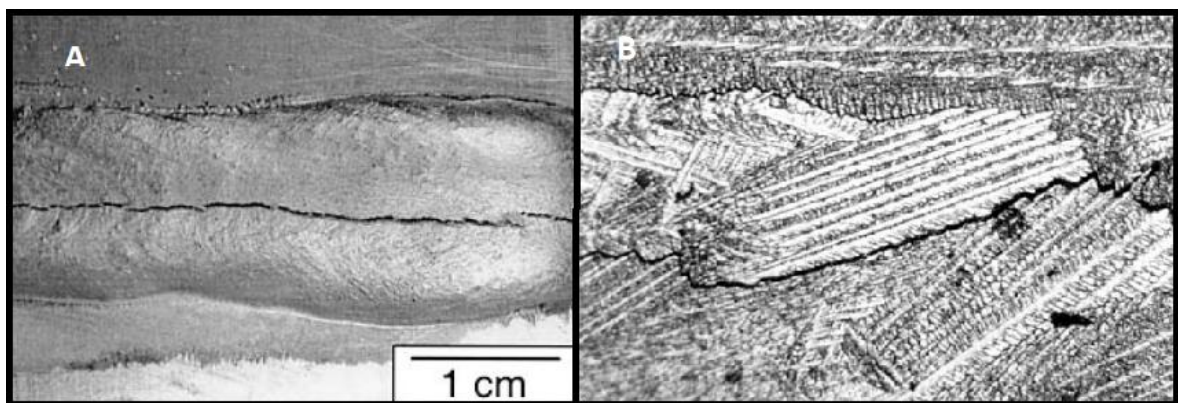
Fissuração a quente A) na soldadura do alumínio 6061 e B) no talão da placa do alumínio 7075 [24].
